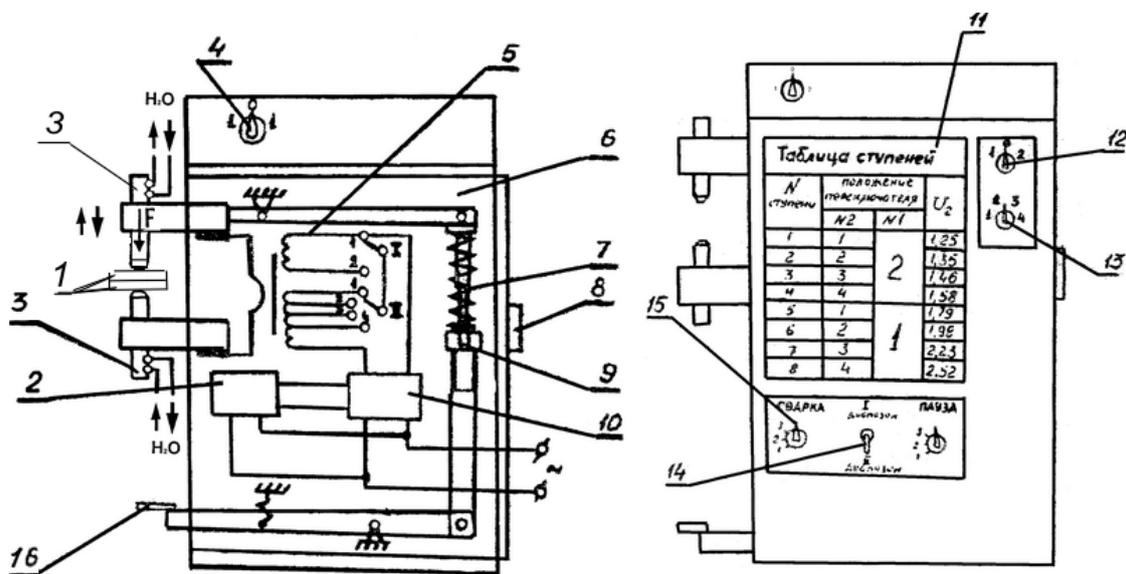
Схема машины МТ-601 для контактной точечной сварки
